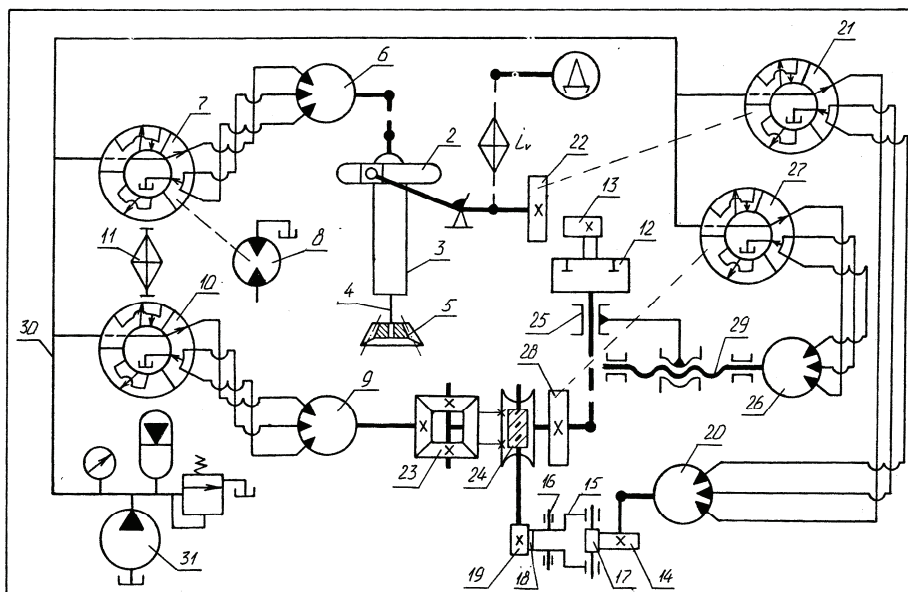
Зубодолбежный станок с гидравлическими связями для нарезания некруглых колес
